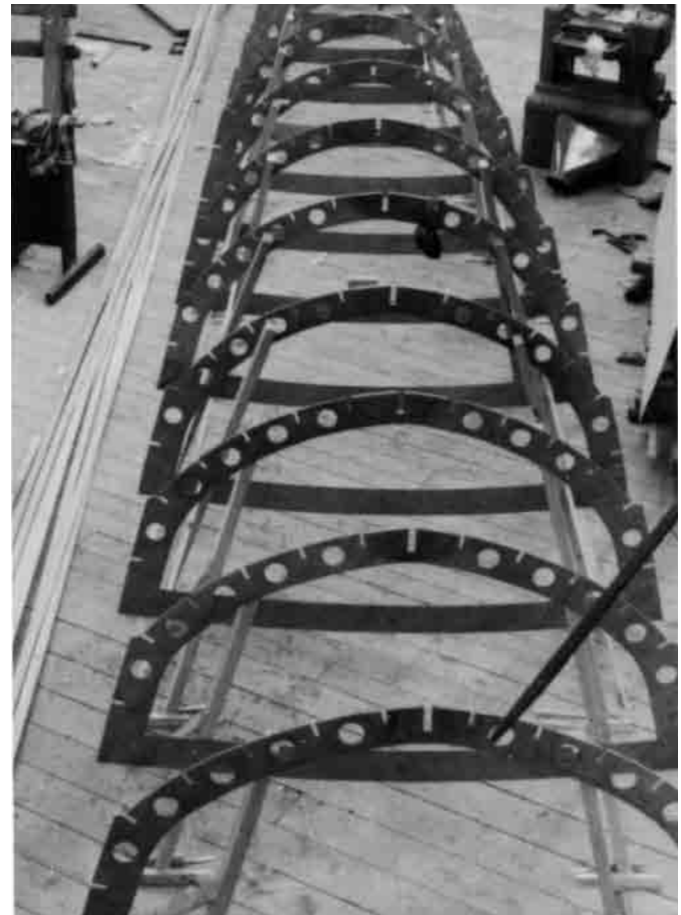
Spanten, aufgestellt für die Proa SLINGSHOT. In diesem Fall wurden die Stringer des Unterwasserschiffs parallel zur Kimm angezeichnet und gegen den Kiel geführt. Der einzige Seitenstringer wurde mittig zwischen Kimm und Balkweger gesetzt.
